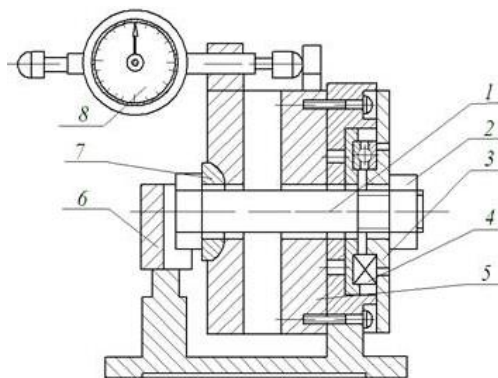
Схема установки: 1 – болт; 2 – гайка; 3 – втулка; 4 – підшипник; 5 – пружина; 6 – стопорний сухар; 7 – шайба; 8 – індикатор
